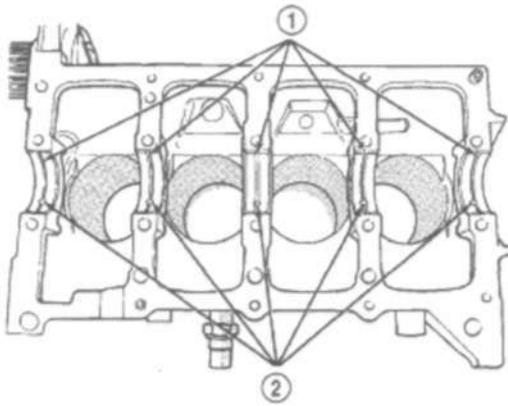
Установка верхнего вкладыша коренного подшипника.
